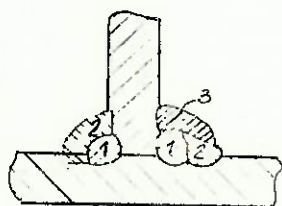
SOLDAGEM EM ÂNGULO EM VÁRIOS PASSES.
